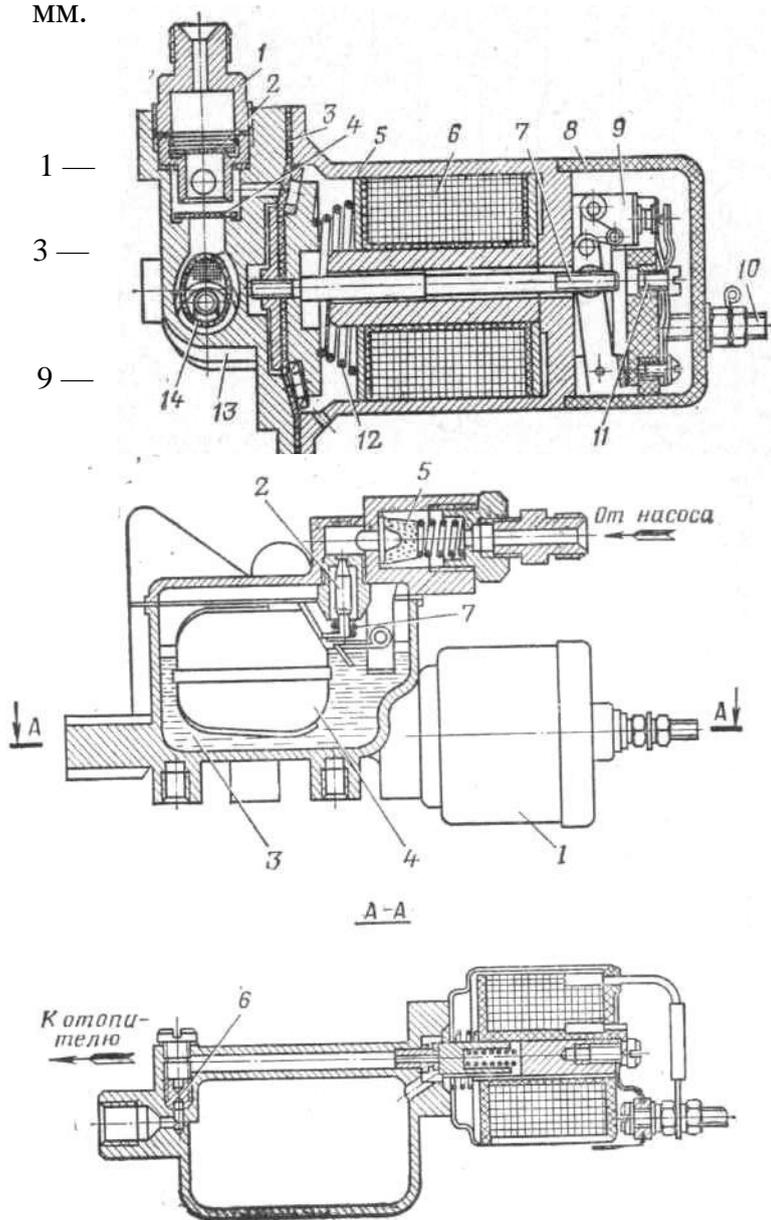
Электромагнитный бензонасос: 1 — выходной штуцер; 2 — нагнетательный клапан; 3 — диафрагма; 4 — впускной клапан; 5 — корпус; 6 — катушка с сердечником; 7 — шток; 8 — крышка контактной системы; 9 — контактная система; 10 — клеммный винт; 11 — регулировочный винт; 12 — ружина; 13 — головка; 14 — фильтр
